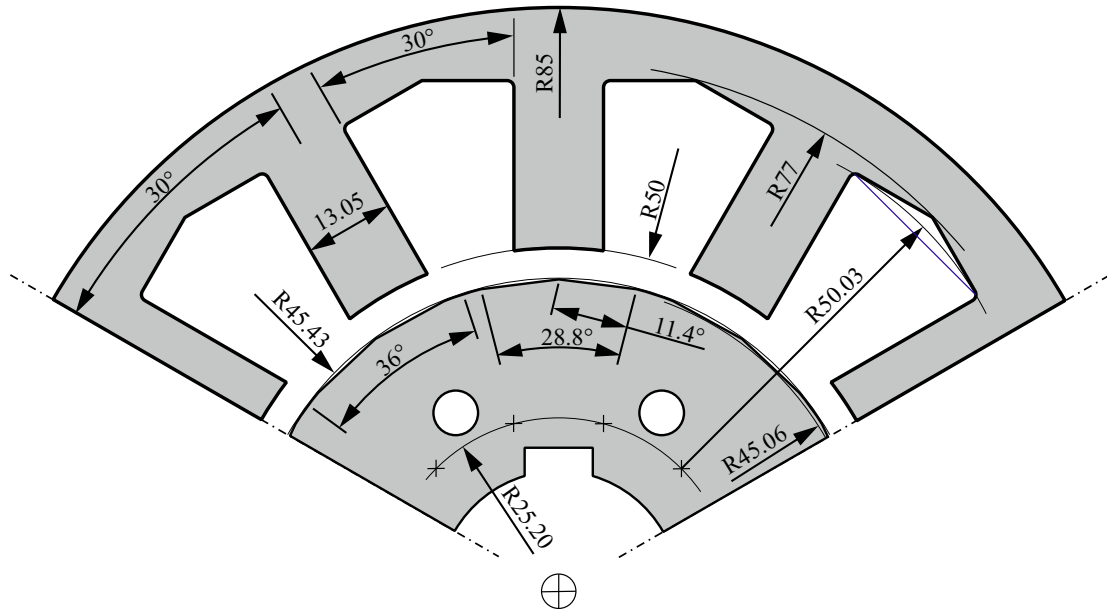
Dimensionen des Stator- und Rotorbleches
